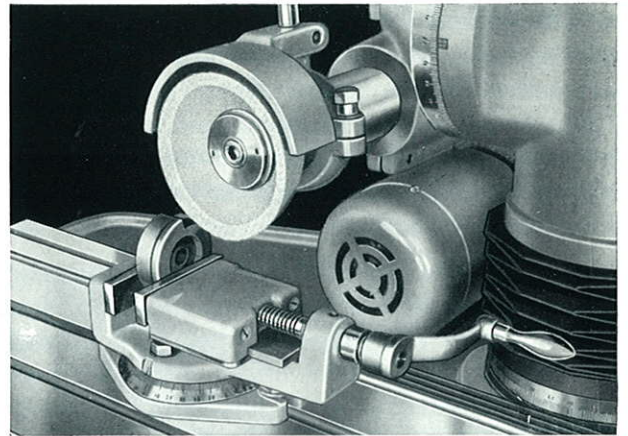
Schleifen eines Formscheibenstahles mit dem Maschinenschraubstock
